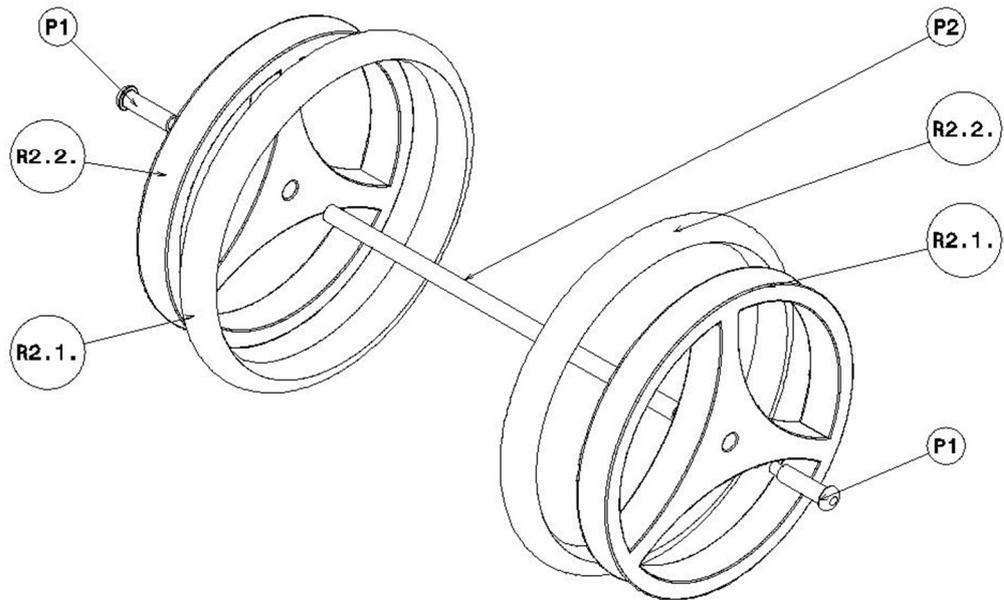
Explosión en vista isométrica del subensamblaje ruedas para escalera.
